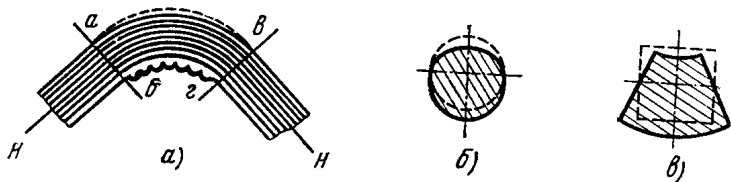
Схема изменения волокон (а) и формы поперечного сечения (б, в) заготовки при гибке
